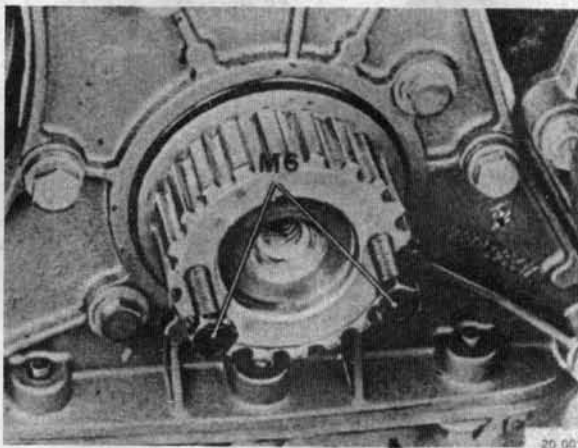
Снятие шестерни привода механизма газораспределения с коленвала
